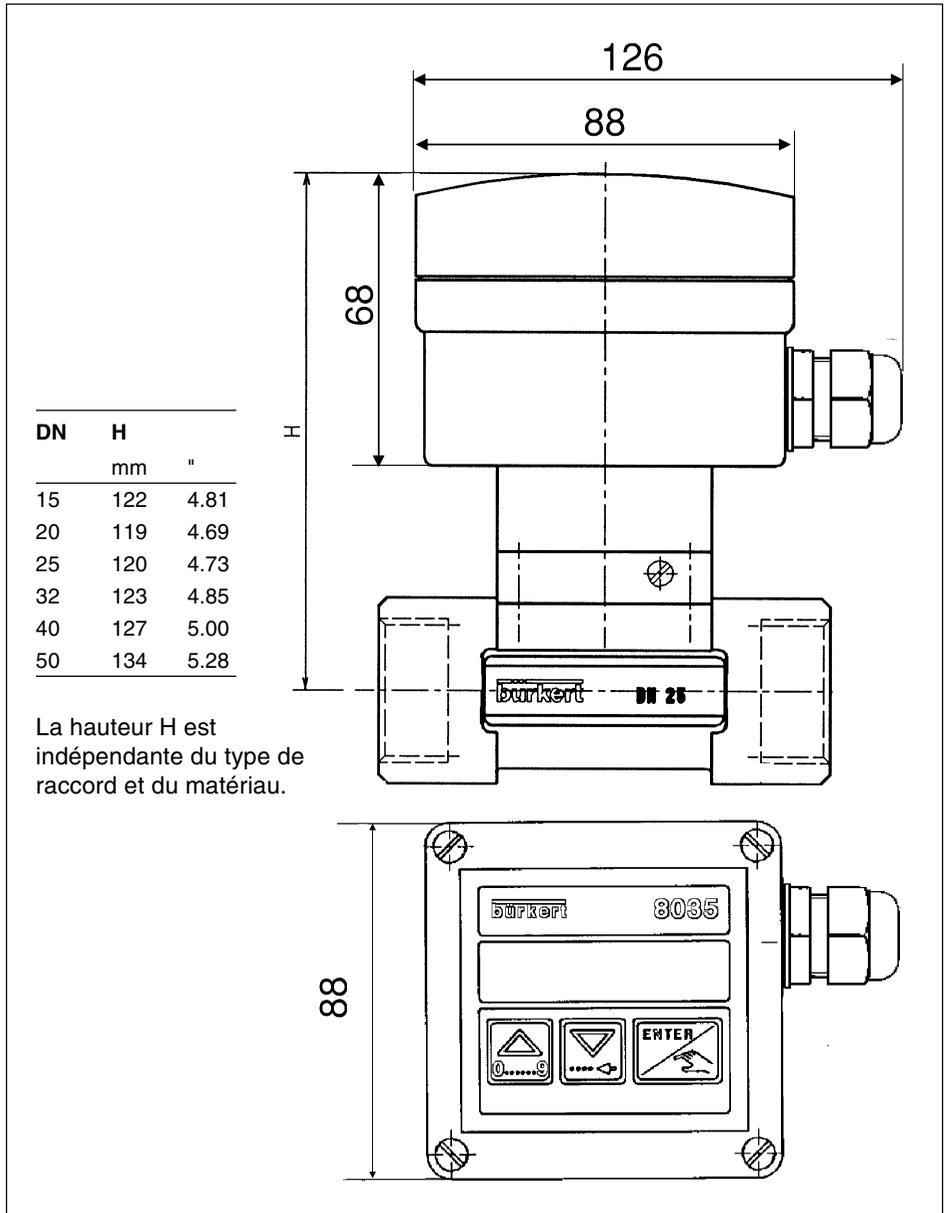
Transmetteur électronique 8035 dimensions externes
